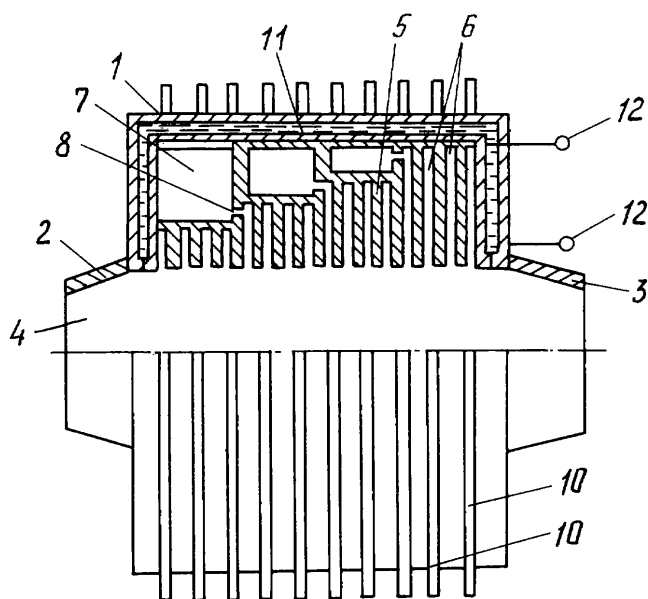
Общий вид глушителя-генератора и его разрез
